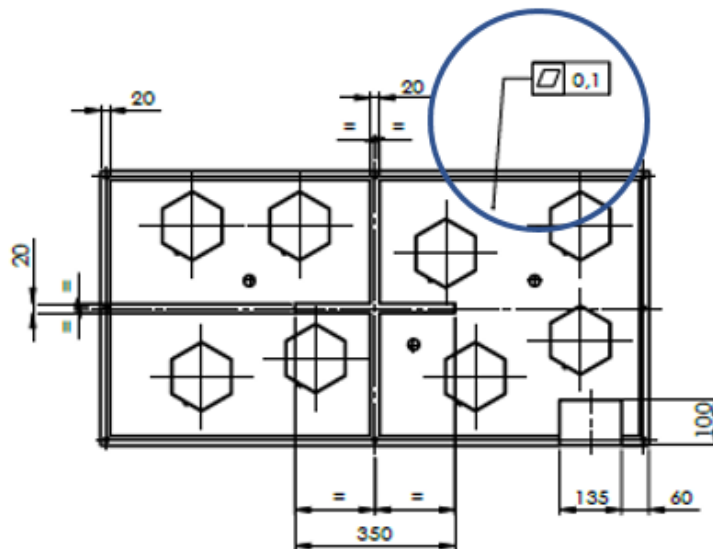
Tolerancia de Planitud de Panel estructural
